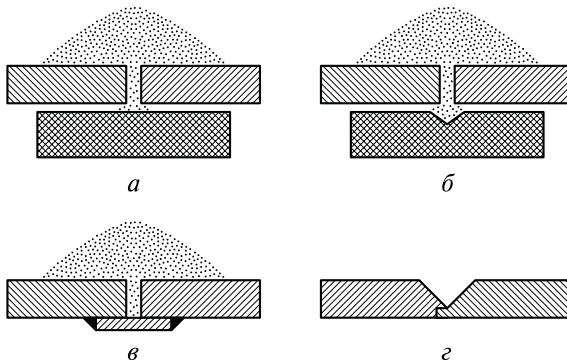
Подкладки для сварки стыковых швов:
